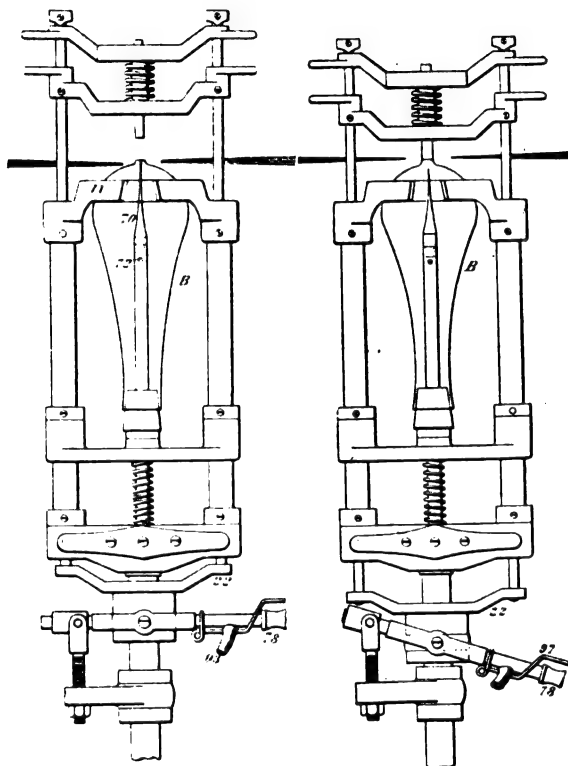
et 37. — Machine Lean et Massy. Fonctionnement du tube 72.
